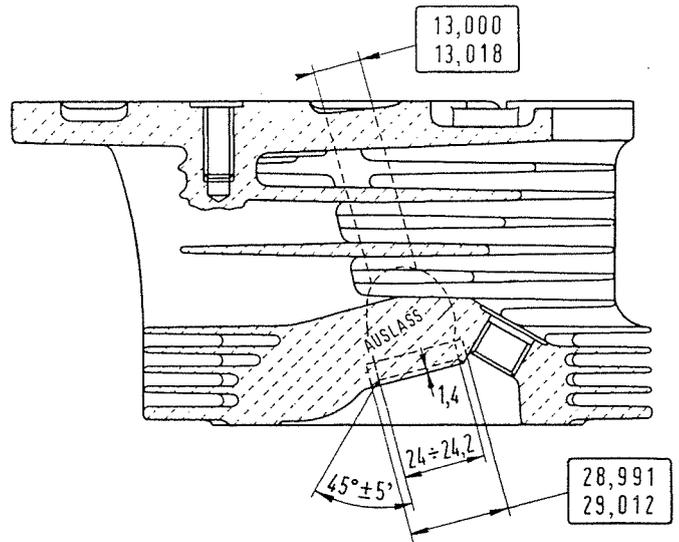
Hauptabmessungen der Auslassventilsitze im Zylinderkopf.
